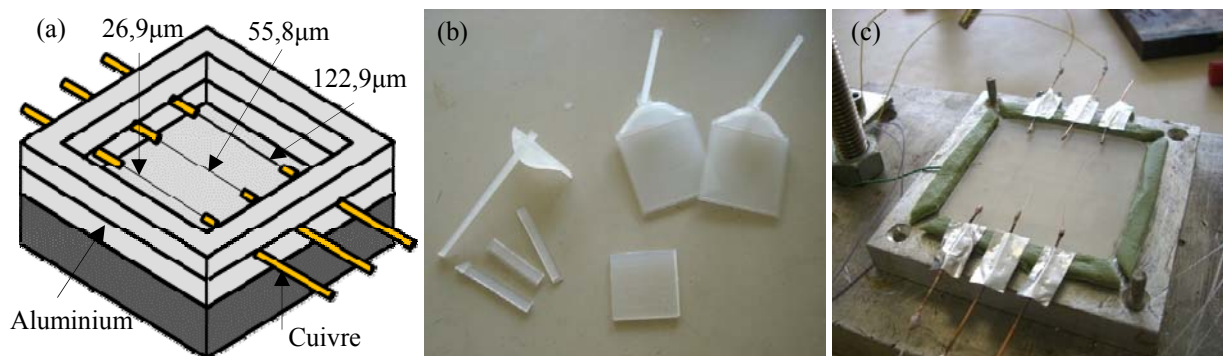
Fabrication des échantillons : (a) schéma du moule (b) plaques de thermoplastique (c) positionnement des fils de nickel soudés dans le plan de joint
